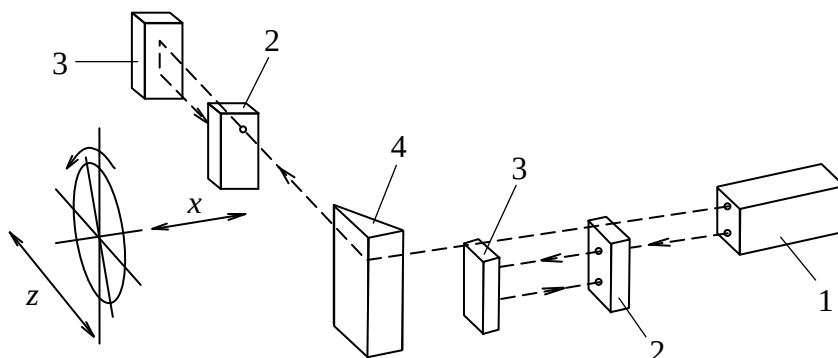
Кинематика рабочих движений токарного центра МК6521Ф3.04: 1 — гелий-неоновый лазер; 2 — интерферометр; 3 — уголкового отражателя; 4 — поворотное зеркало
